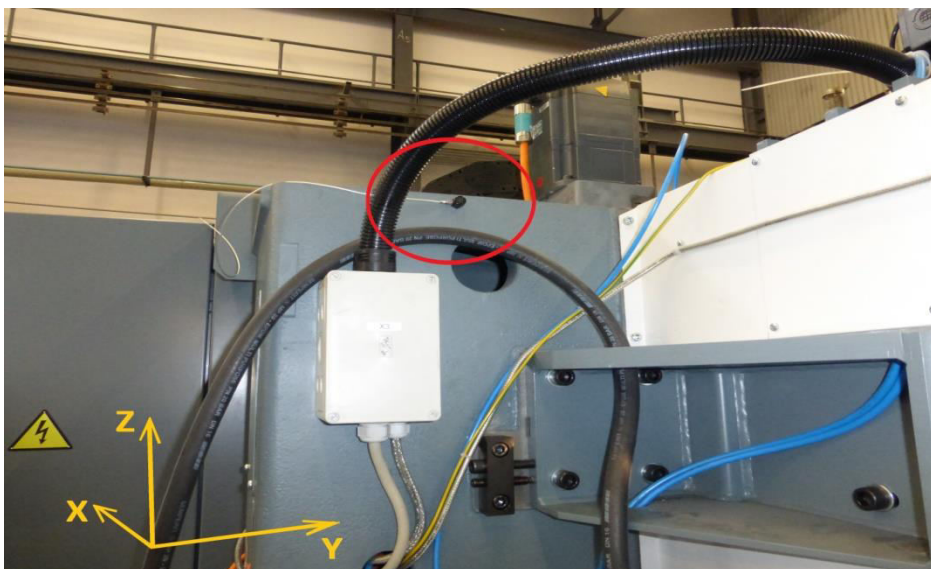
Priebeh druhej zaťažovacej skúšky
